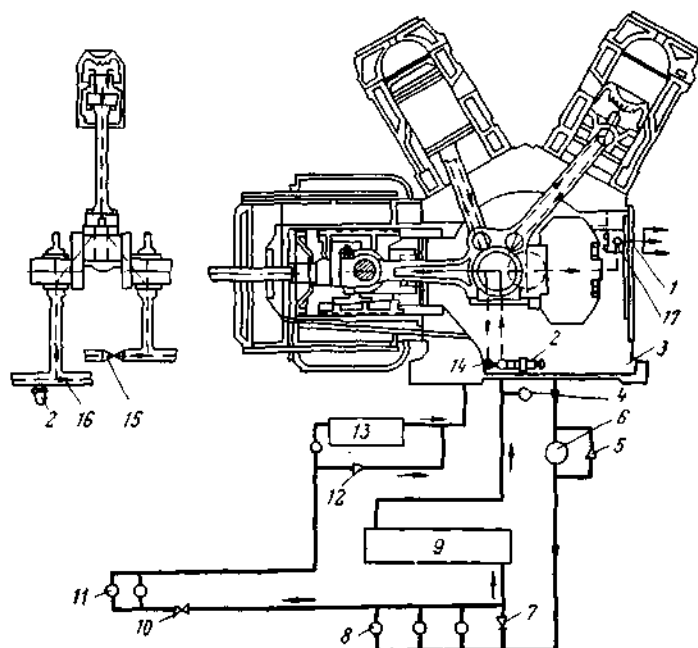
Схема смазки газомоторного компрессора 10 ГК:
